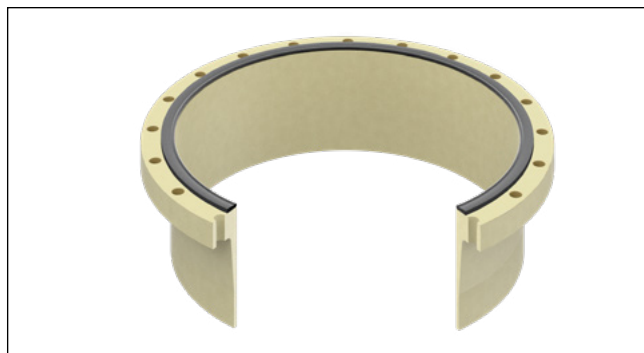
Profileret ringpakning (betragtes som hævet overflade for momentindstilling)
